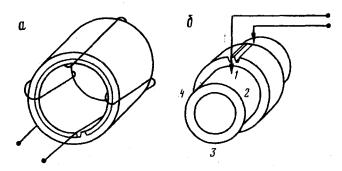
Схема контроля соединительных муфт и зубчатых втулок
